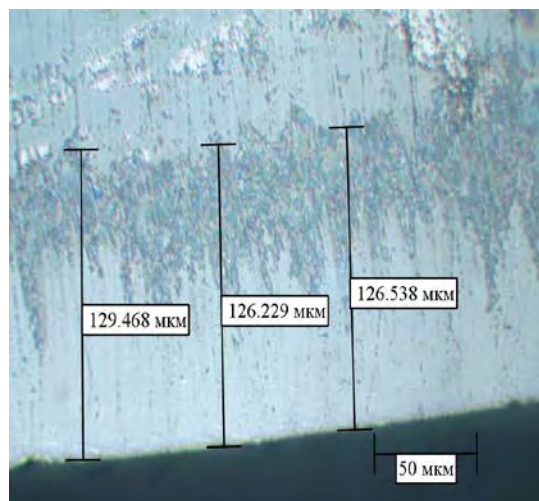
Изображение режущей кромки образца SiAlON с нанесением размеров
